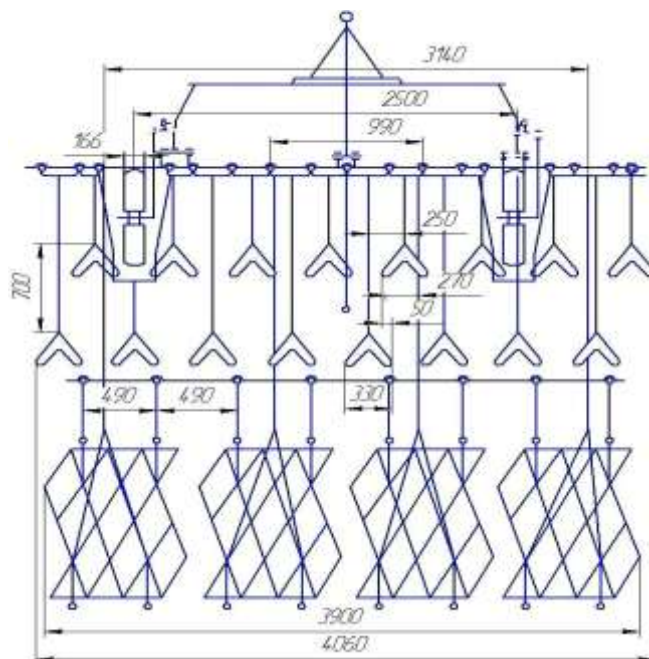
Схема расстановки рабочих органов для сплошной предпосевной обработки
